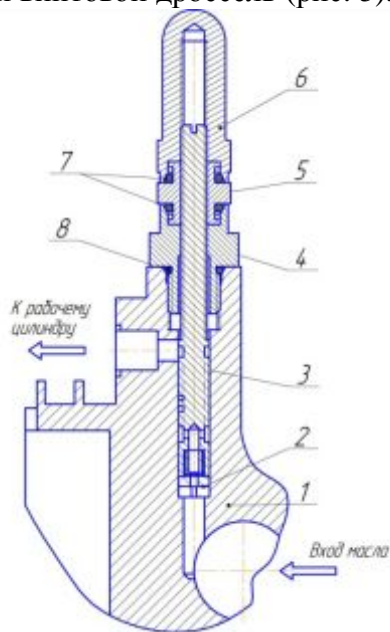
Конструктивная схема регулируемого винтового дросселя: 1 – корпус АУП; 2 – местный дроссель с гидравлическим сопротивлением, равным штатному жиклёра-втулки; 3 - игла винтового дросселя; 4 – штуцер; 5 – втулка; 6 – колпак; 7, 8 - уплотнительные кольца
